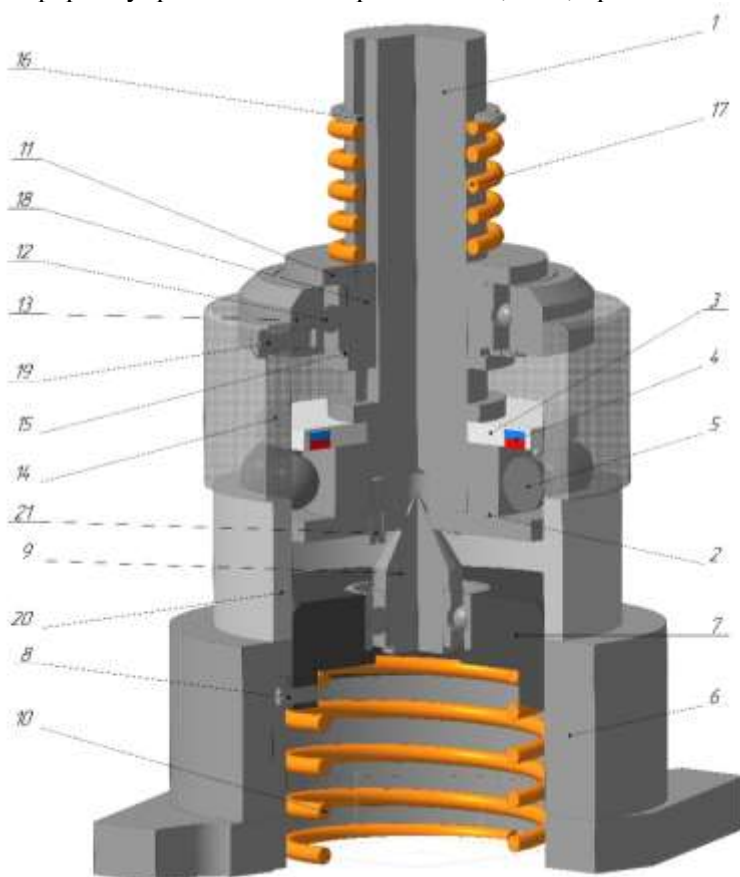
Конструкция устройства для поверхностного пластического деформирования внутренней поверхности жесткой втулки
